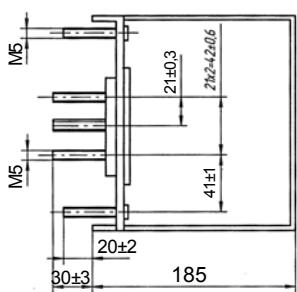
Габаритные, установочные и присоединительные размеры блоков конденсаторов типов БК-401, БК-402.
